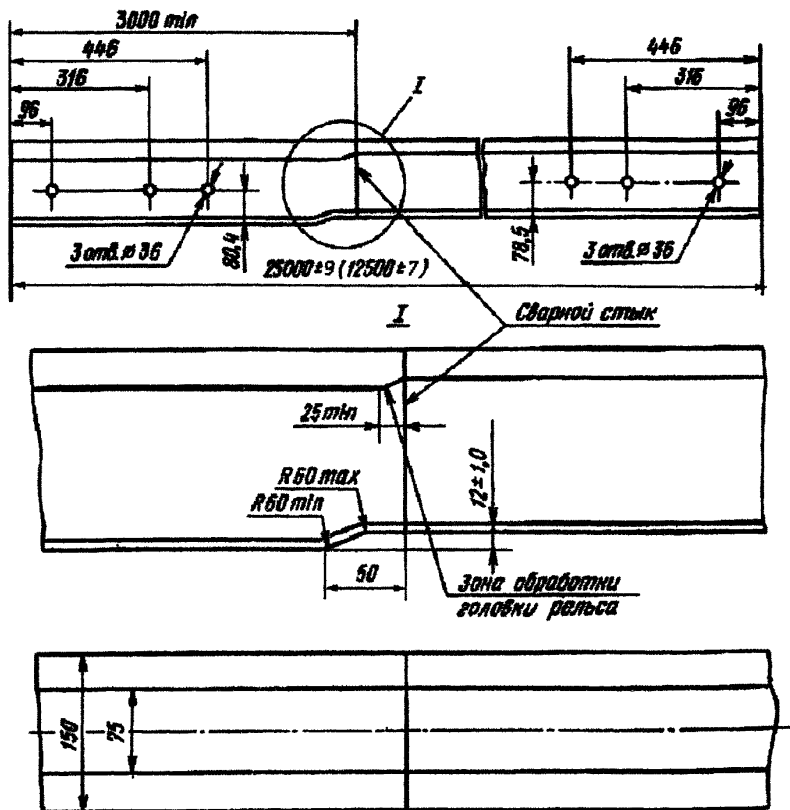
Конструкция и размеры сварного рельса переходного профиля с типа Р75 на Р65
